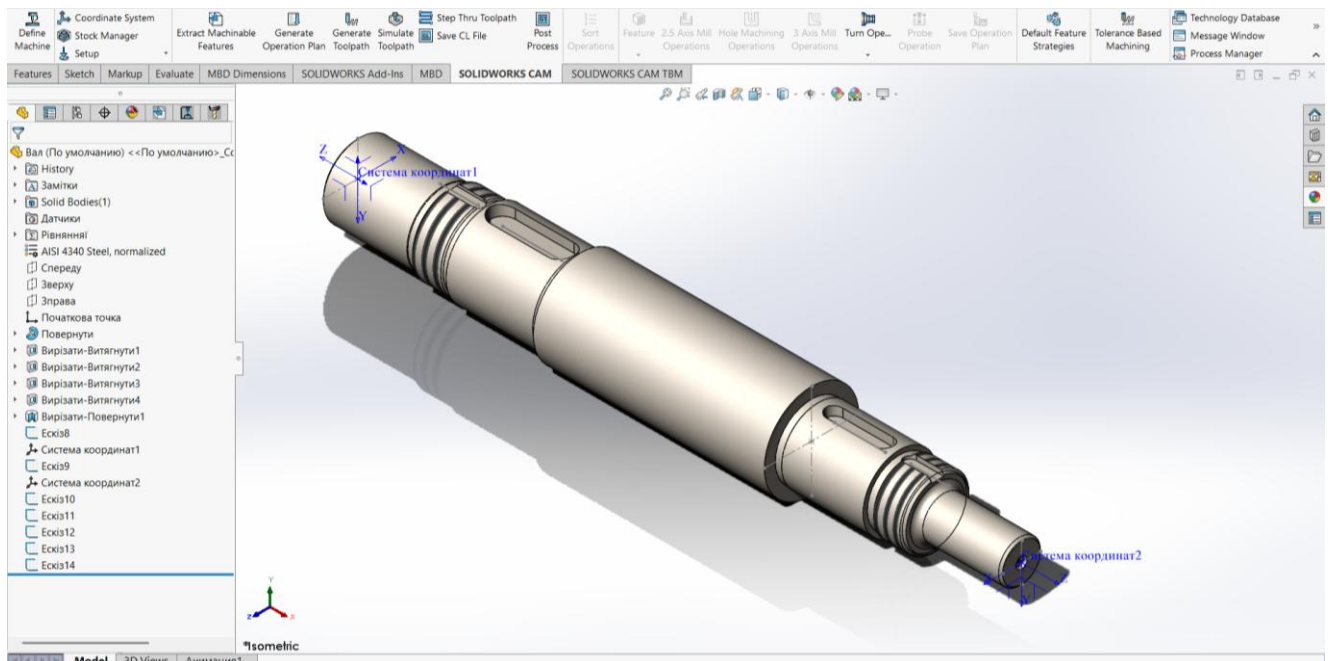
Модель деталі «Вал МР ПМ 629.00.002/24»
